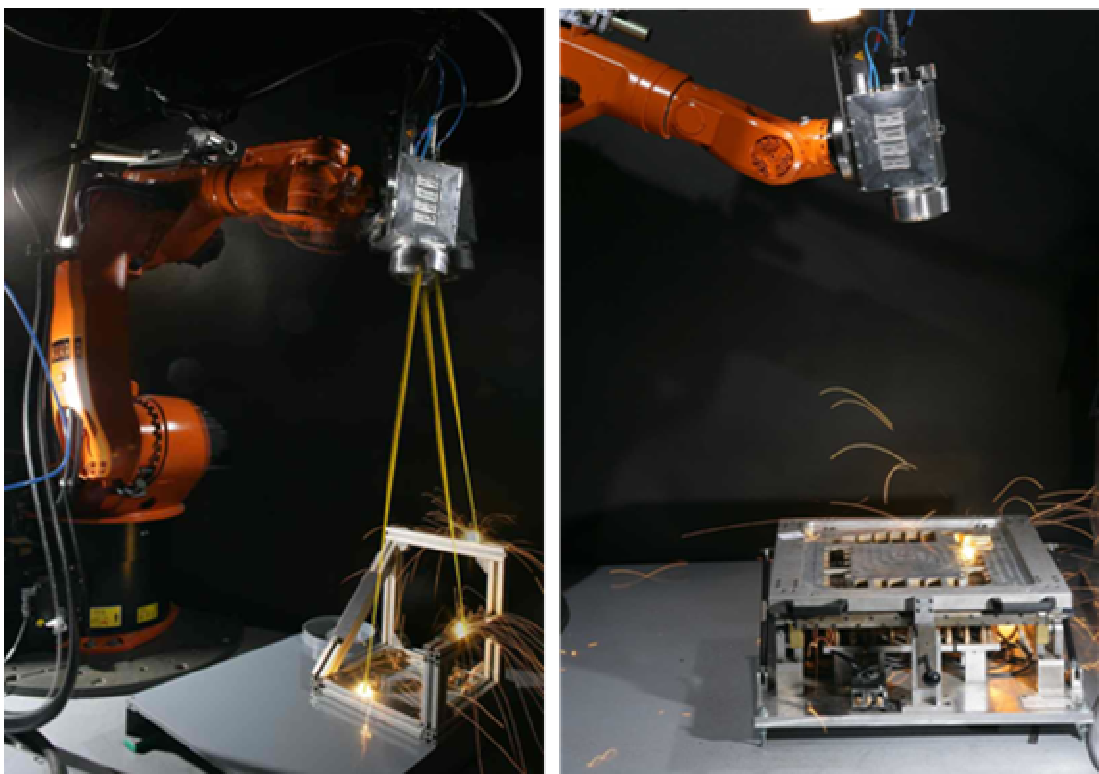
Laserstrahlschweißen mit RoboScan und Zoomoptik am Beispiel Sitzfertigung
